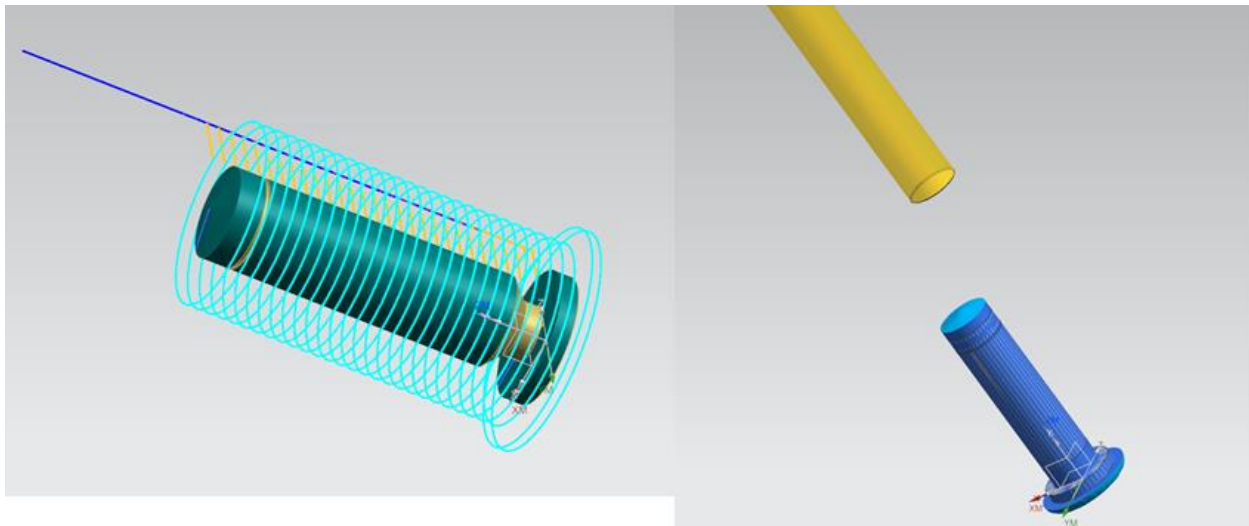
Фрезерування зовнішніх поверхонь
